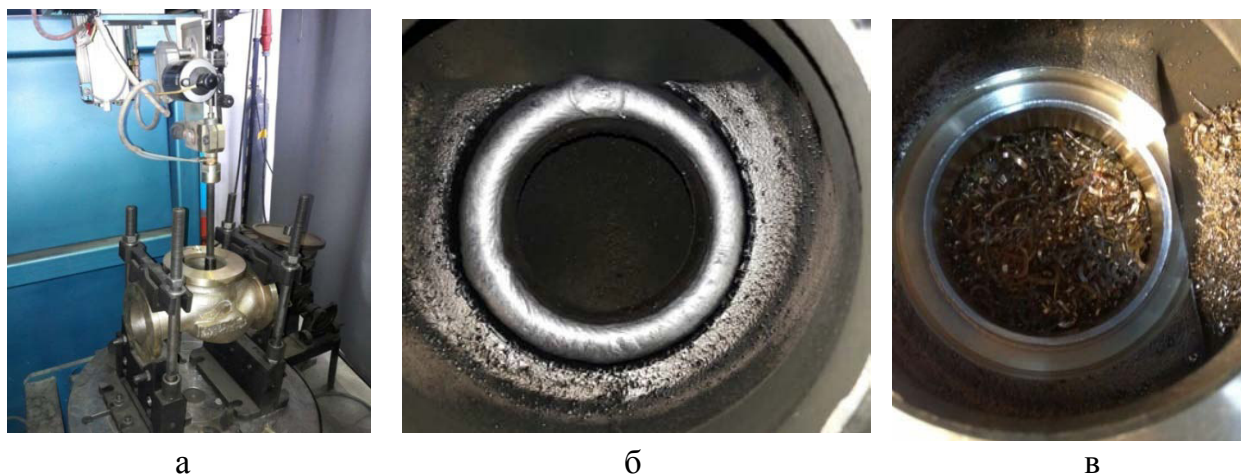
Уплотнительное поле судовой арматуры из бронзы БрА9Ж4Н4Мц1 после автоматической наплавки на него сварочной проволоки Св-МНЖМцТК 40-1-1-0,3-0,1
